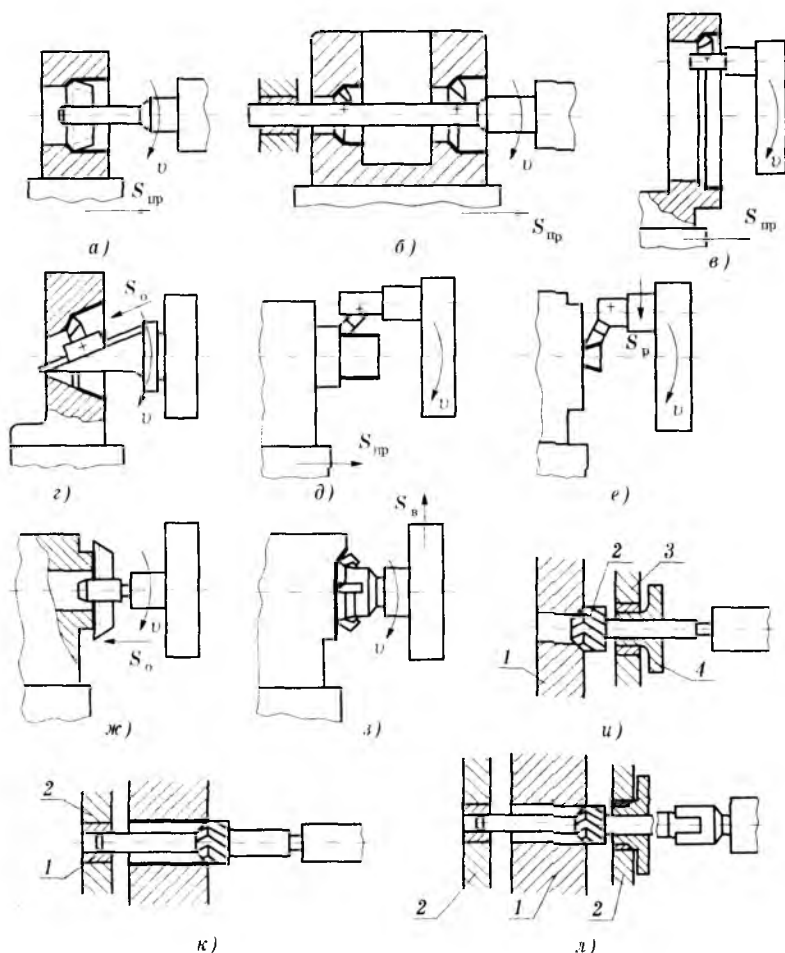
Схемы обработки заготовок на расточных станках:
